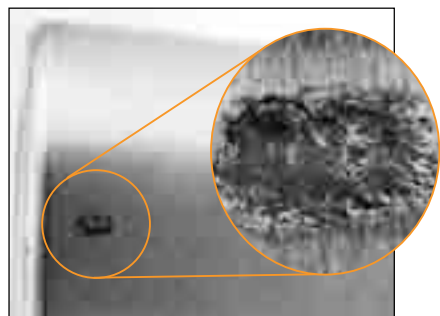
图中放大10倍后的电弧灼坑或微小灼痕，是由于轴承静止时接地不当，产生电弧造成的。
